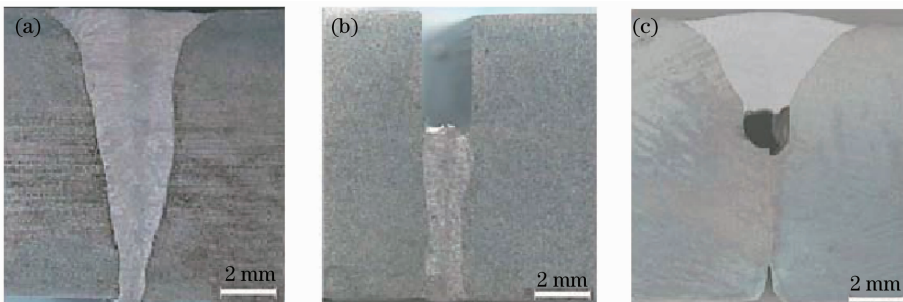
焊缝横截面。(a)复合焊接;(b)激光焊接;(c)电弧焊接
